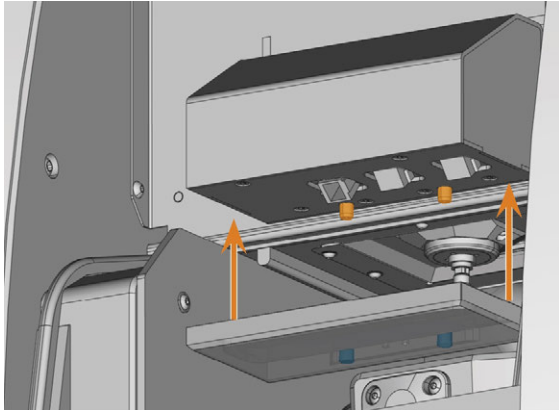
INSTALAR LA CUBIERTA DEL IONIZADOR (REBAJES MARCADOS EN AZUL Y CLAVIJAS MARCADAS EN NARANJA)
